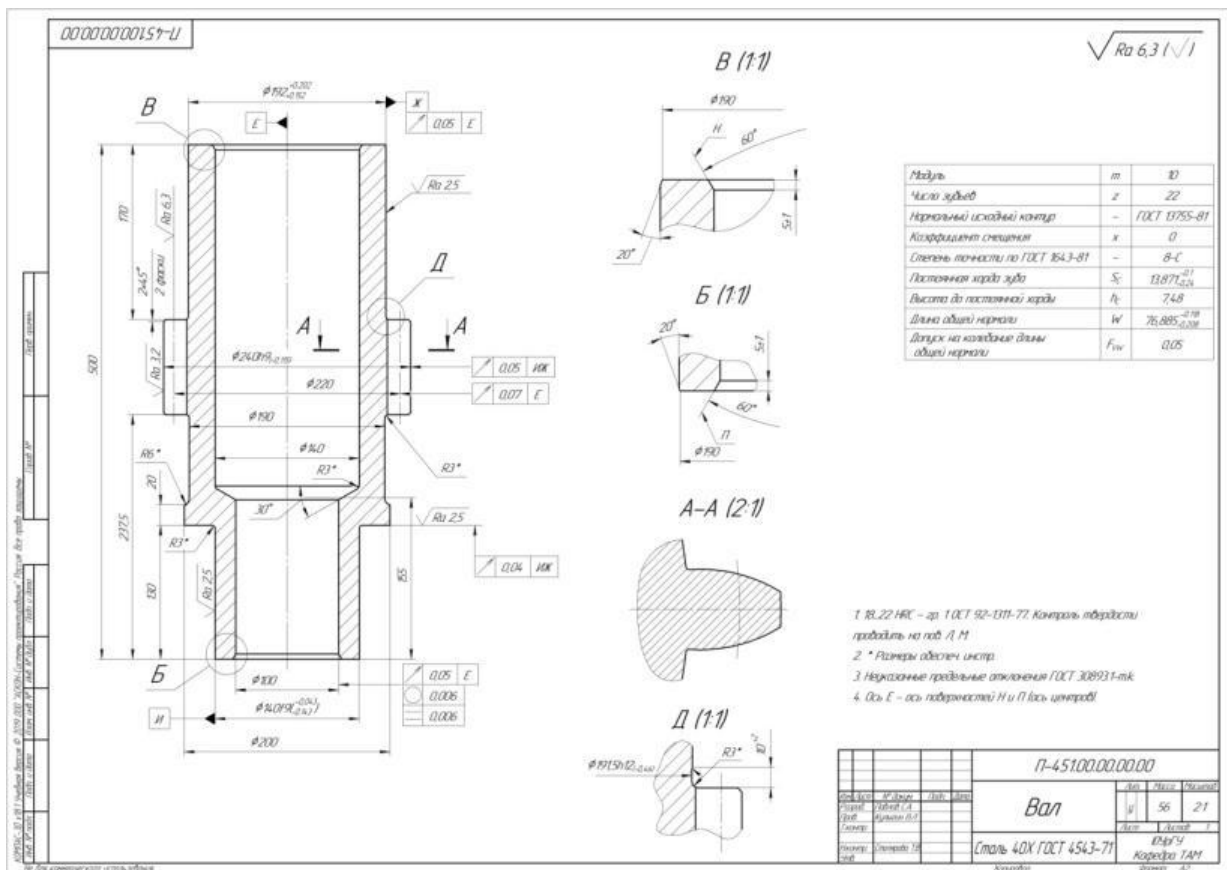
Рабочий чертёж детали «Вал манипулятора гидравлического»
